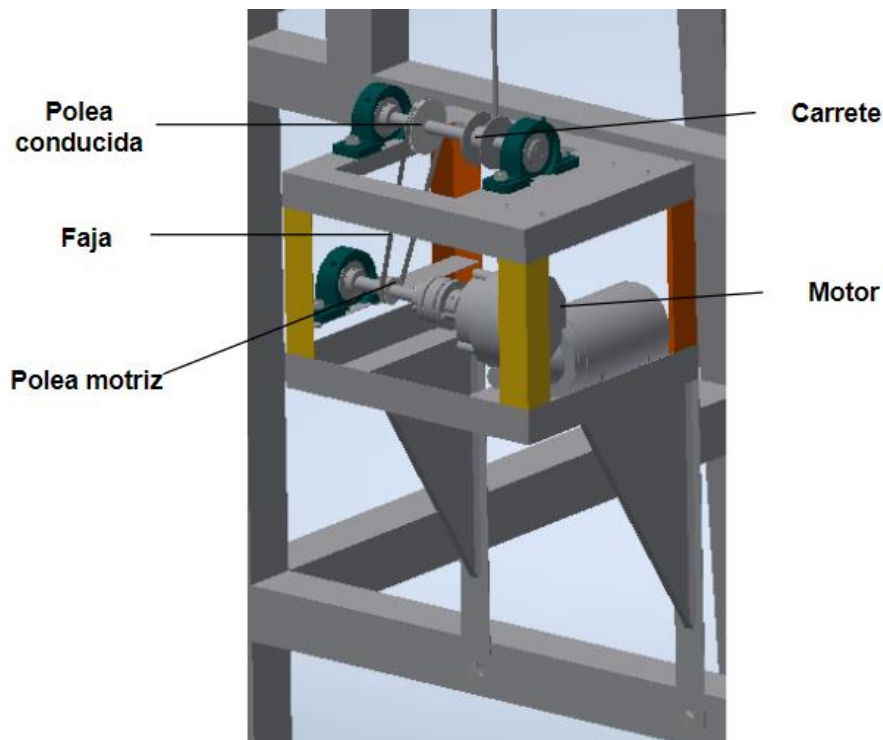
Diseño del soporte del motor y componentes mecánicos.
